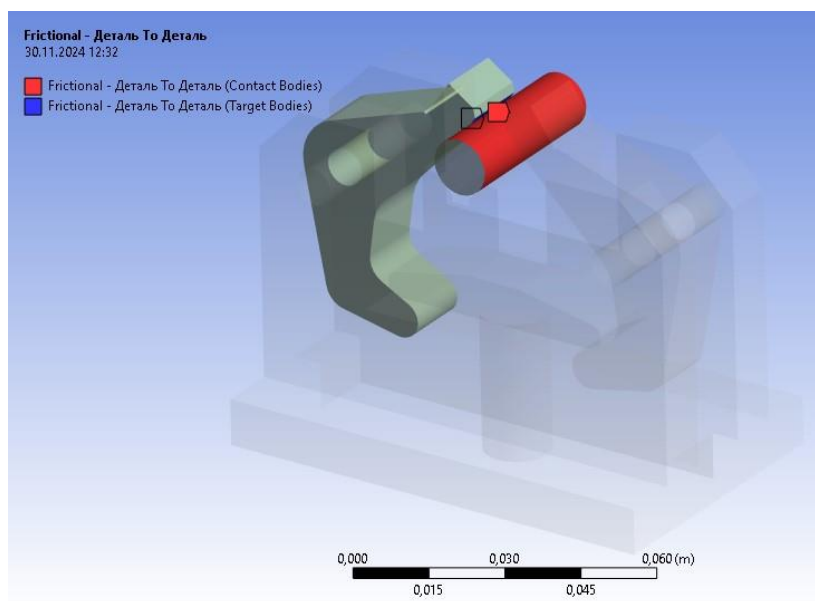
Поверхні контакту циліндричної поверхні заготовки та важіля
